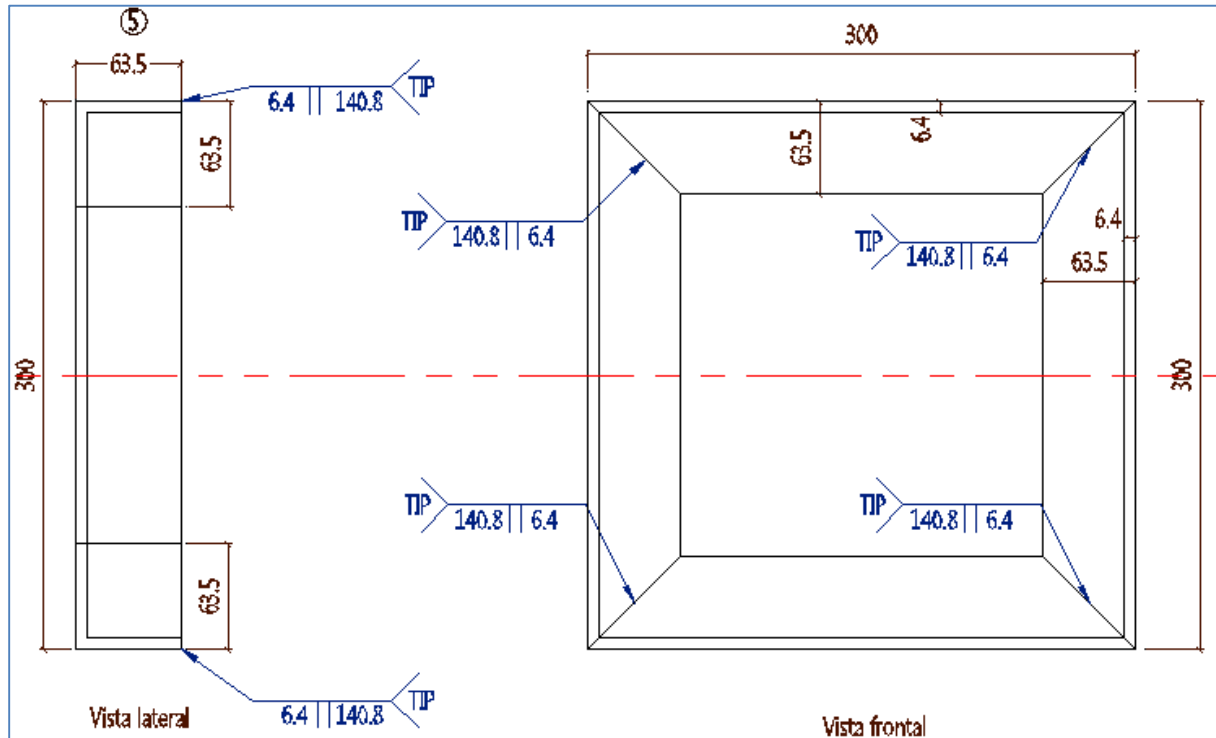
Detalle despiece pieza No.5 modelo 1 flexión.
